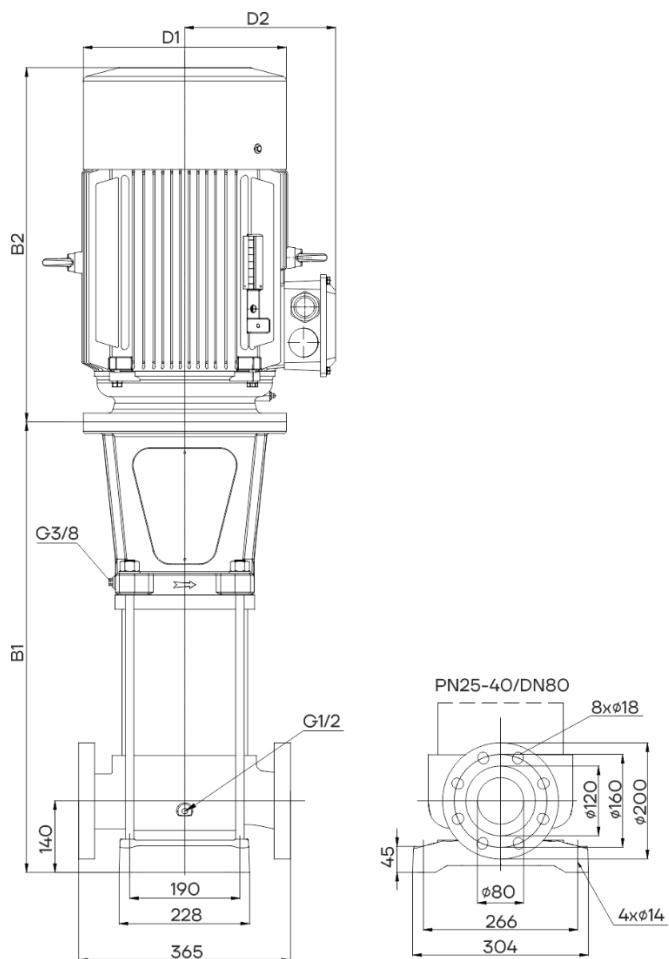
Е Габаритно-присоединительные размеры VMB(F)-H 45
